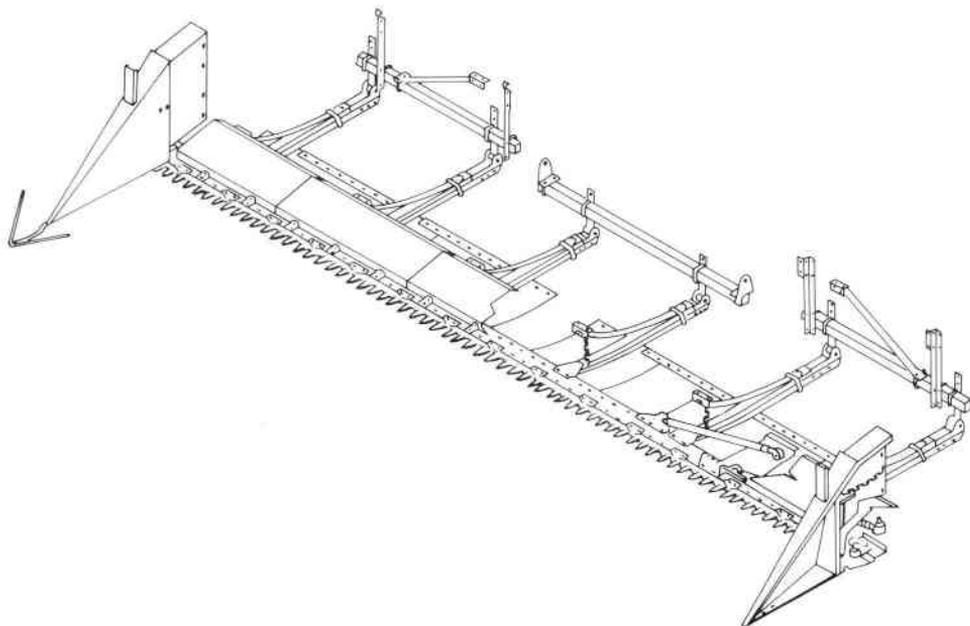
Vue générale d'une barre de coupe flottante.
